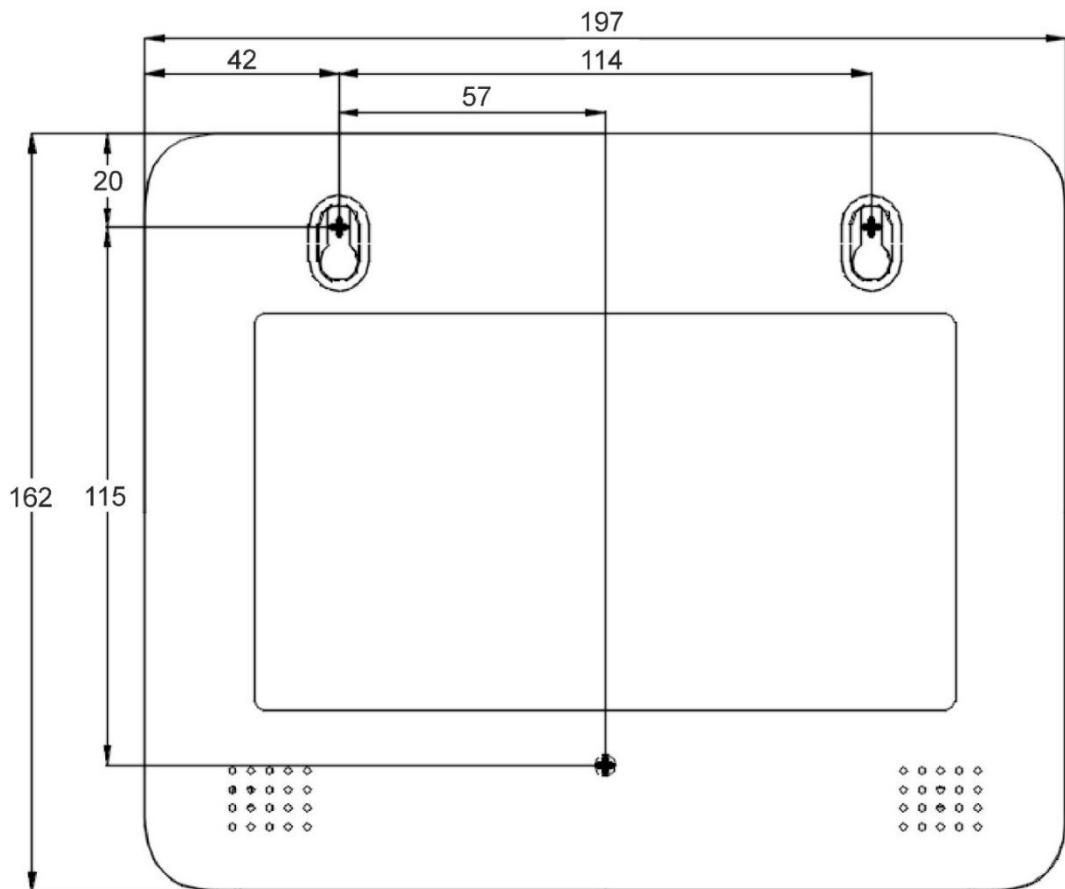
Разметка отверстий для крепления прибора КОП-02.6, КОП-01(8), КОП-01 исп.1 и КОП-04 (вид со стороны передней панели)
